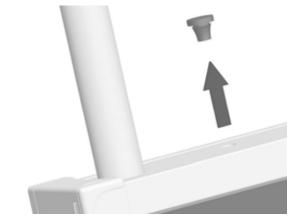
Stopfen vorsichtig aus dem Kollektorgehäuse entfernen.
